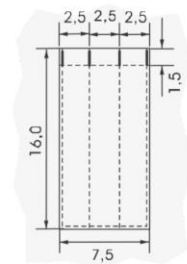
Detalhes do bolso auxiliar tipo caneteiro
